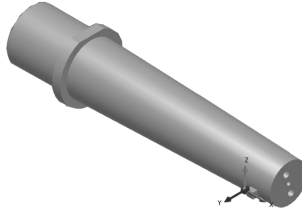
Розрахункова схема пружної системи супортної групи токарного верстата
